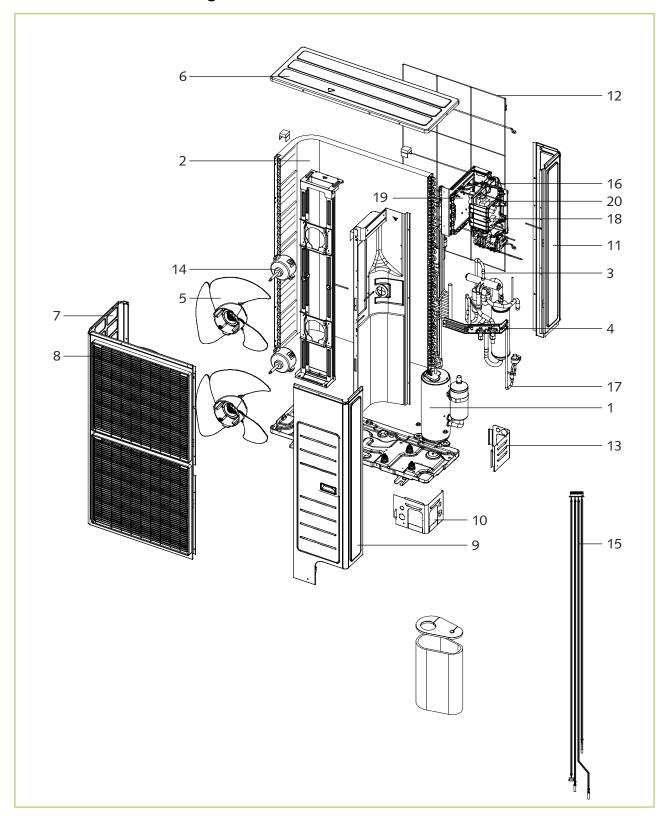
Explosionszeichnung Außenmodul CMF 180 Duo
